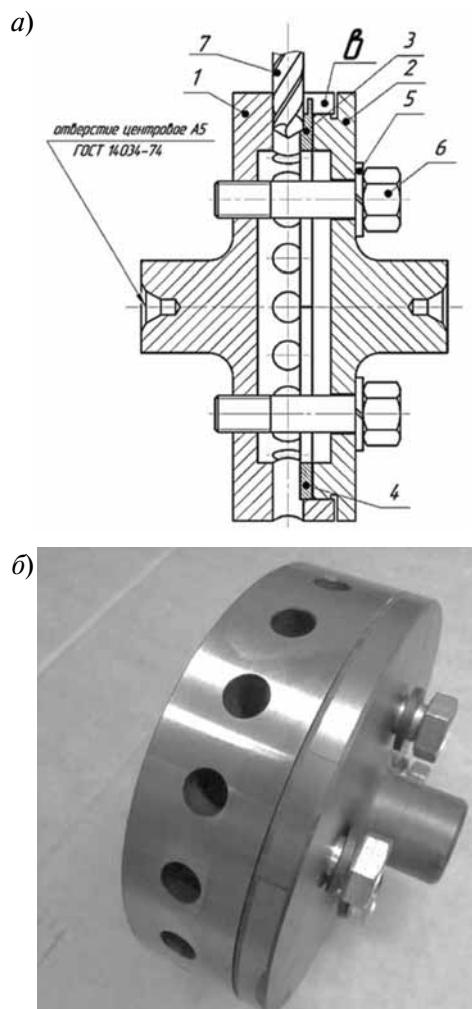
Эскиз (а) и фотография (б) изготовленного кондуктора:
